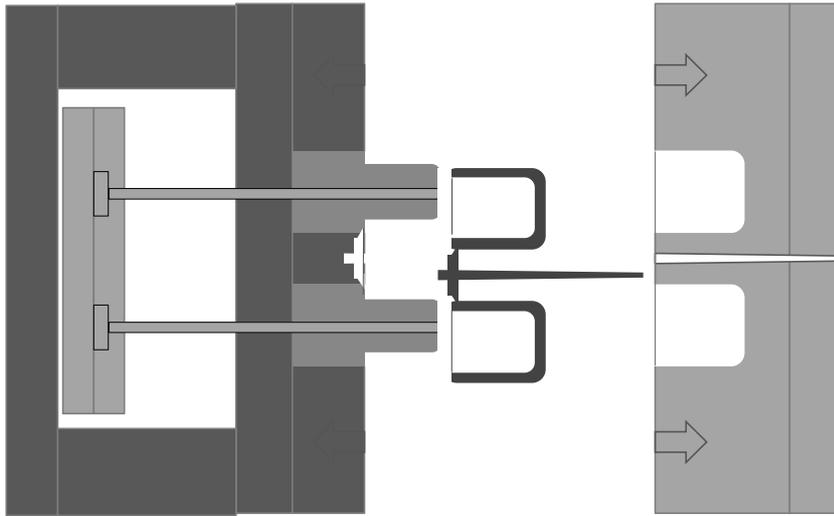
Becherwerkzeug mit Punktanguss – geöffnet
